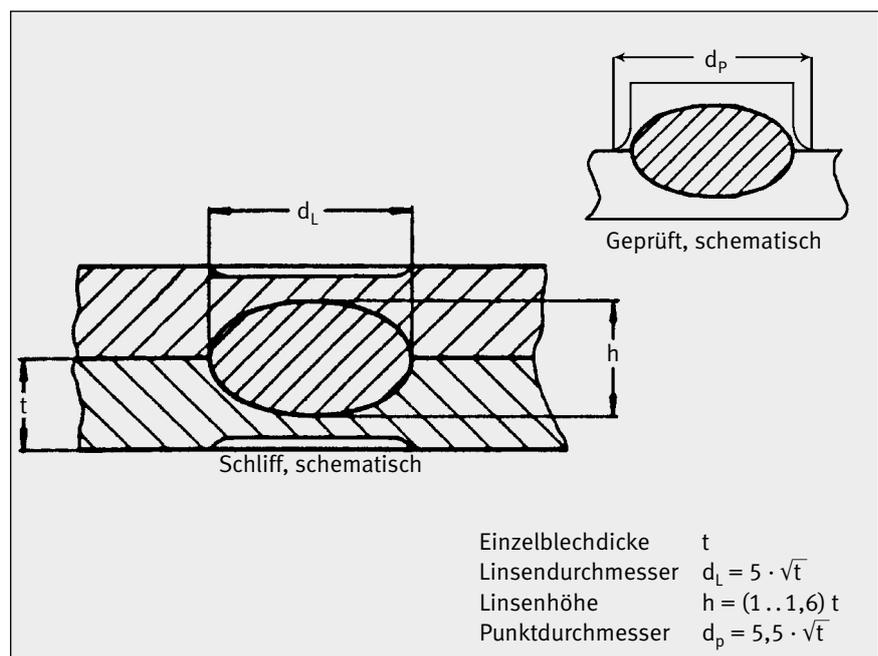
Angaben für empfohlene Abmessungen beim Widerstandspunktschweißen
